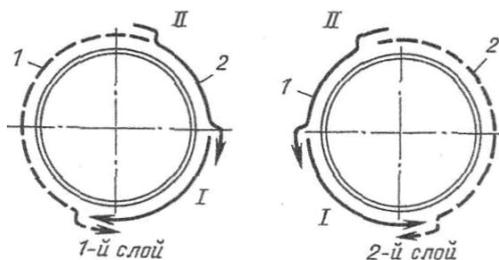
Схема наложения двух слоев шва при сварке сверху вниз двумя сварщиками:
